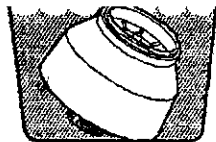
Мойка корпуса регуляторов VRM и VRR
